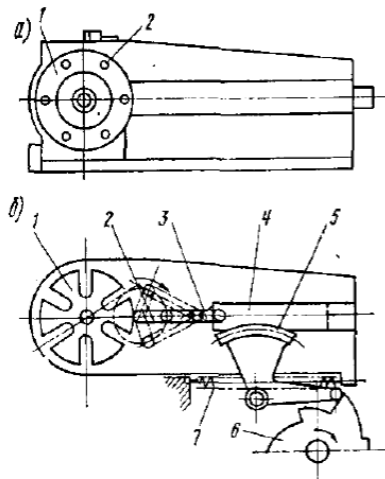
Пример поворотного устройства – револьверная головка автомата 1Б136.
